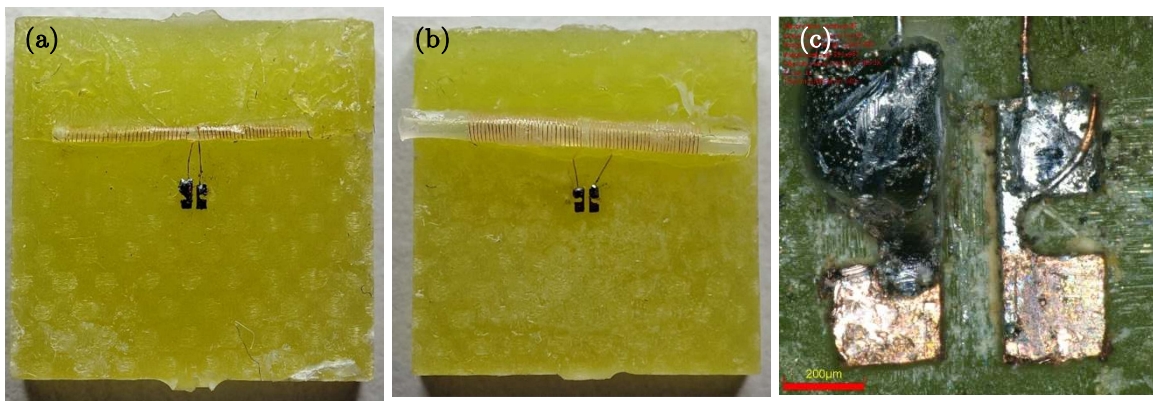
Prototipos de antena de hélice 1Fr (a) y 3Fr (b) soldados a una PCB y detalle de la soldadura (c).
